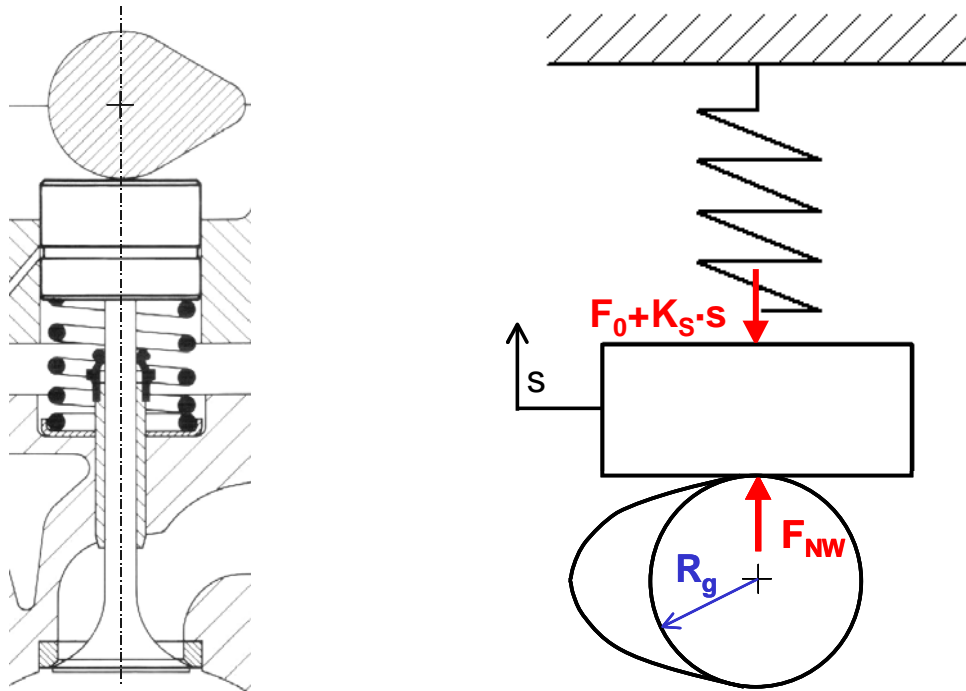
Tassenstößelventiltrieb und Ersatzsystem
